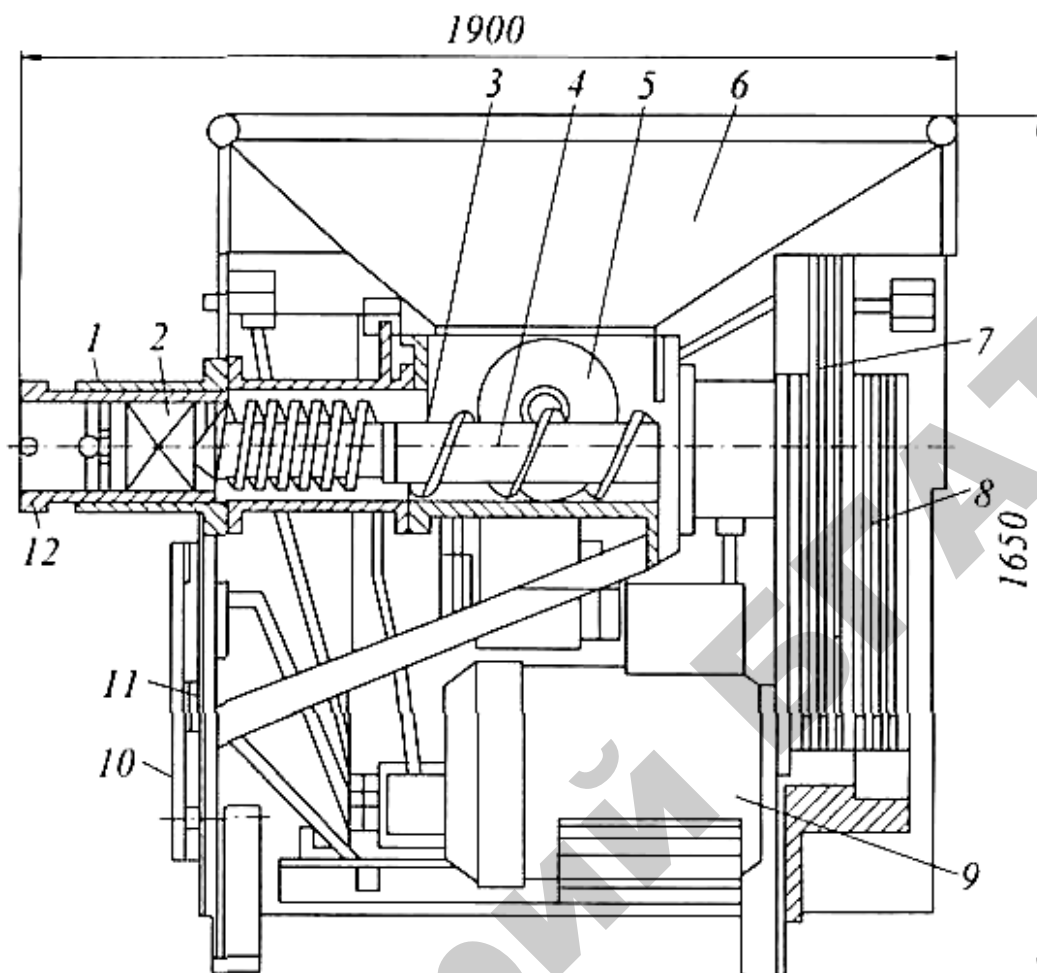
Схема волчка К7-ФВП-160-2:
